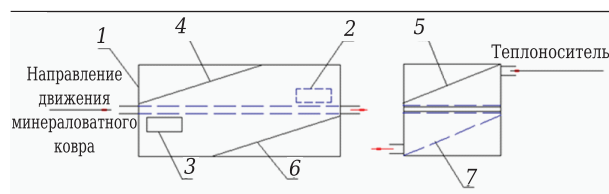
Схема реконструкции внутренней части тепловой камеры: 1 — тепловая камера; 2 — входной патрубок; 3 — выходной патрубок; 4 — верхняя продольная пластина; 5 — верхняя поперечная пластина; 6 — нижняя продольная пластина; 7 — нижняя поперечная пластина
